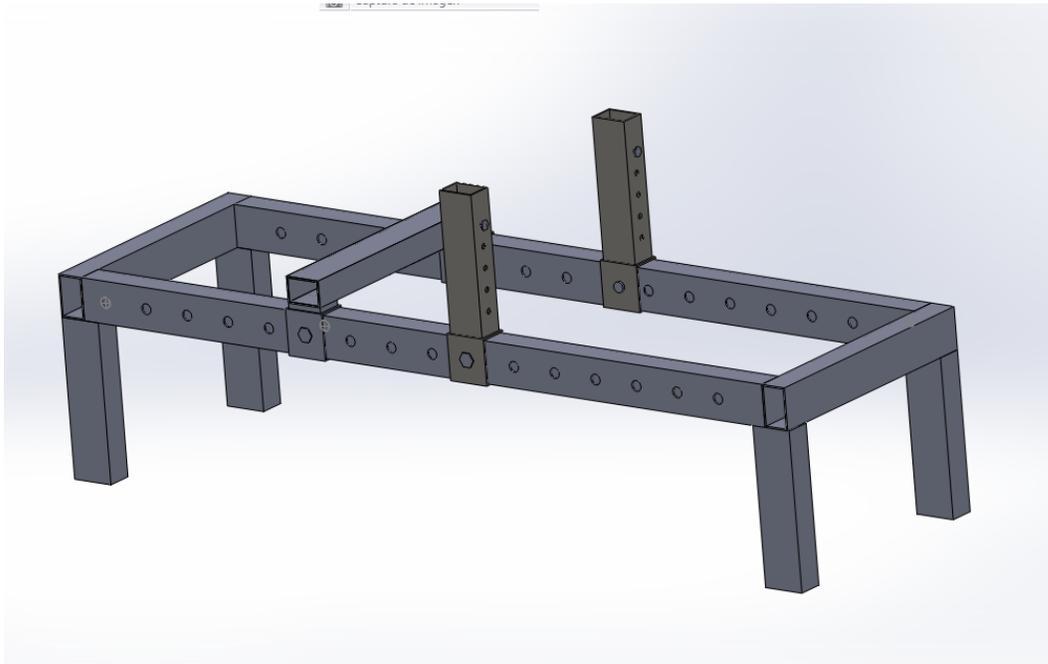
Dibujo en CAD del diseño de la estructura del banco.
